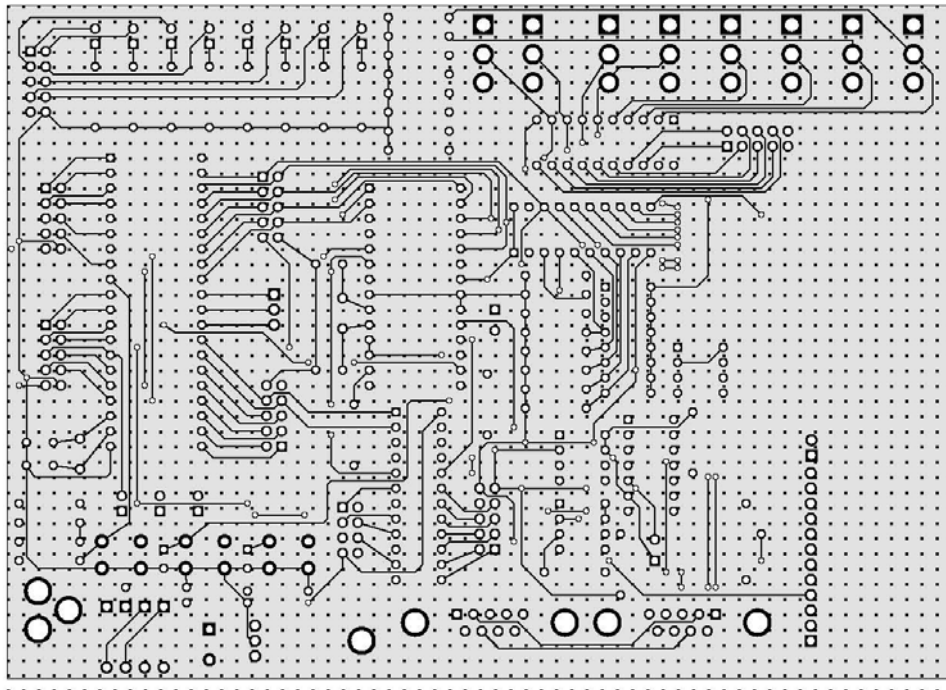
Diagrama PCB de la parte de soldadura del SeeCAN (*Bottom layer*).
